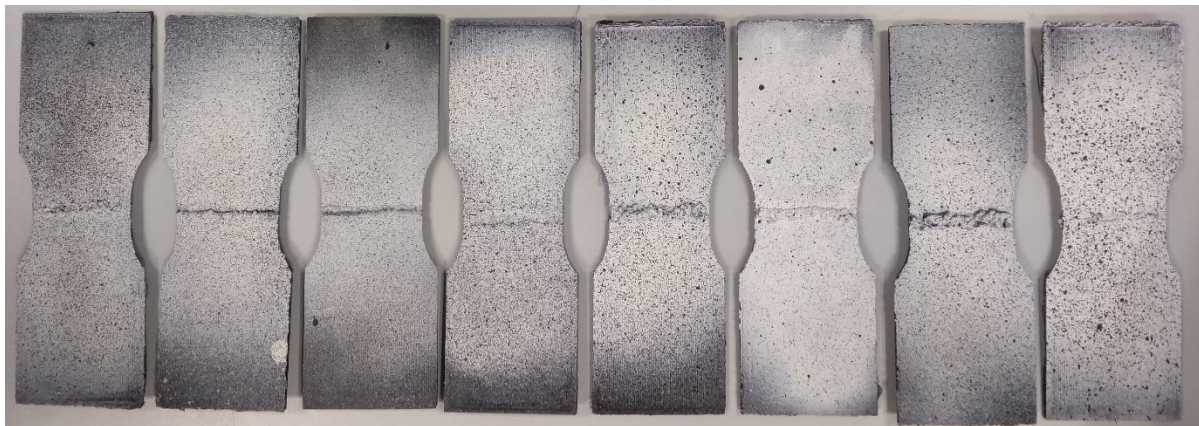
Probetas soldadas preparadas para ser numeradas y ensayadas
